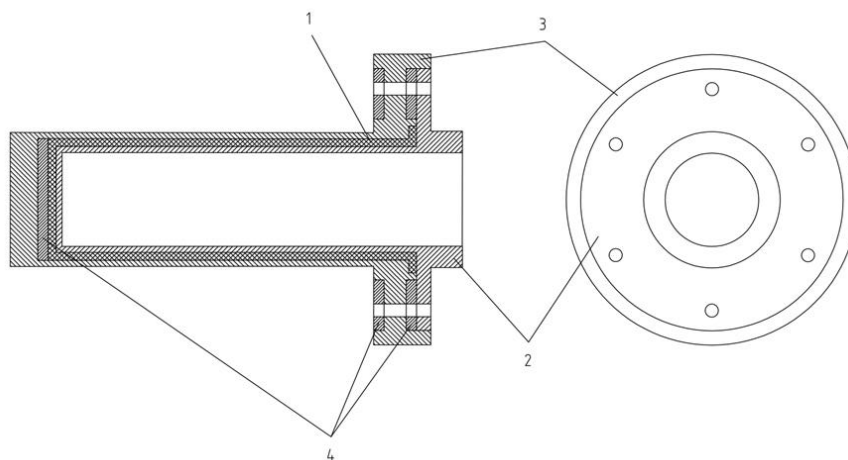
Композитный корпус для магнитореологического демпфера
